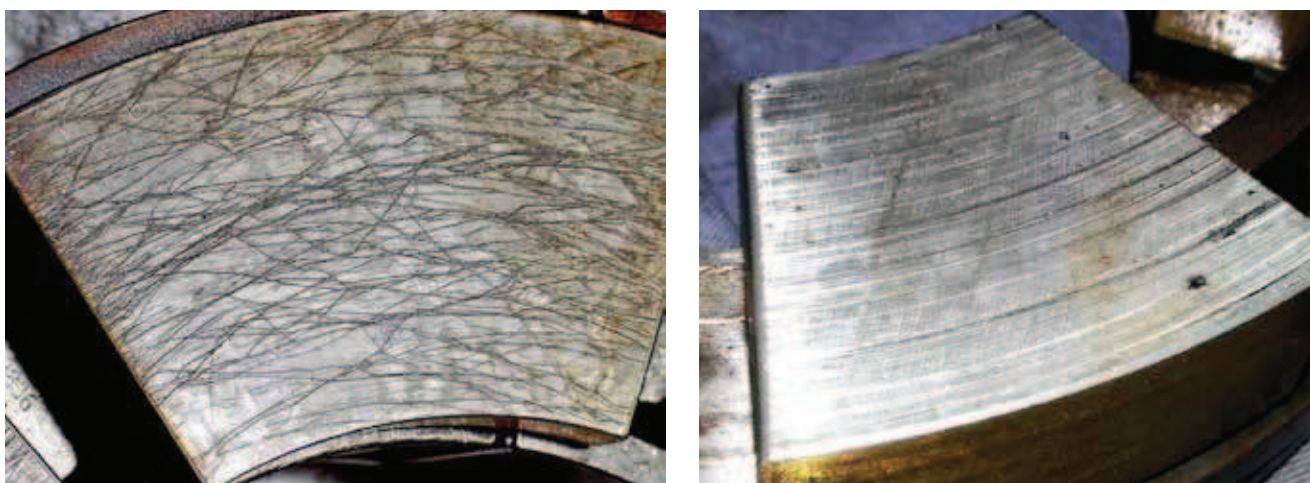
Типичный вид электроэрозии на колодках упорного подшипника
